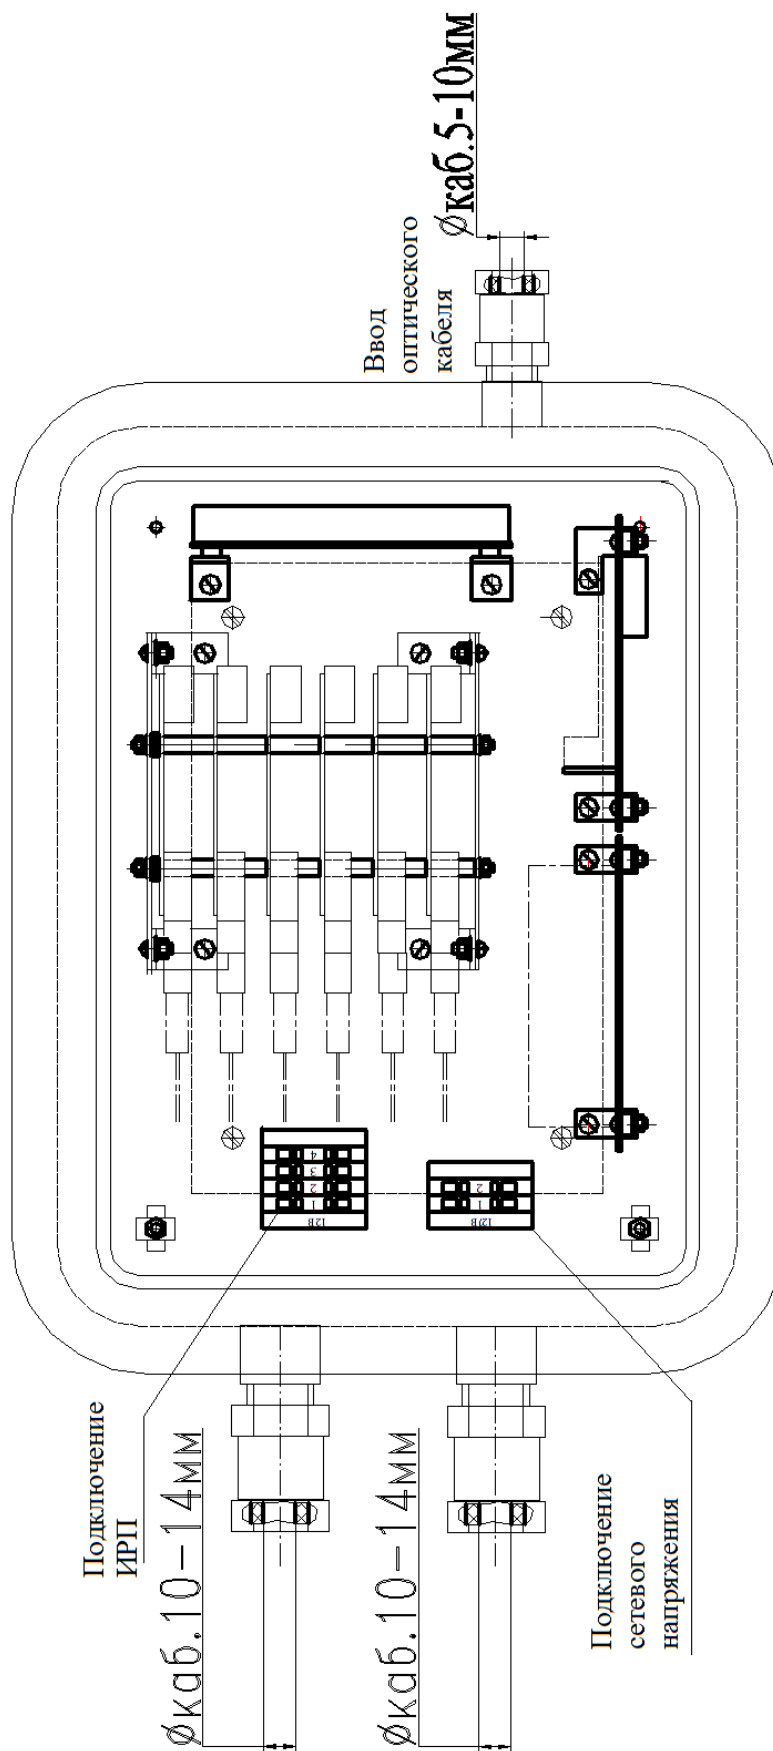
Чертёж корпуса IP-коммутатора со снятой крышкой.
